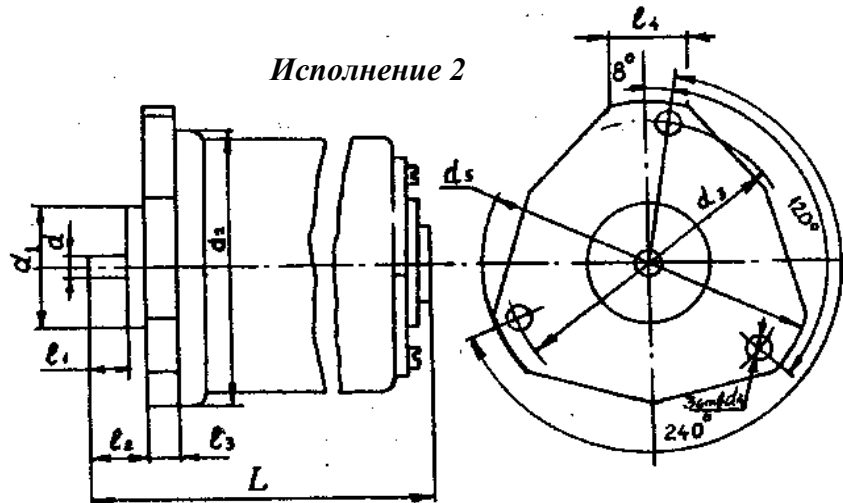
Конструктивные размеры двигателей серий ДИД и ДГ
